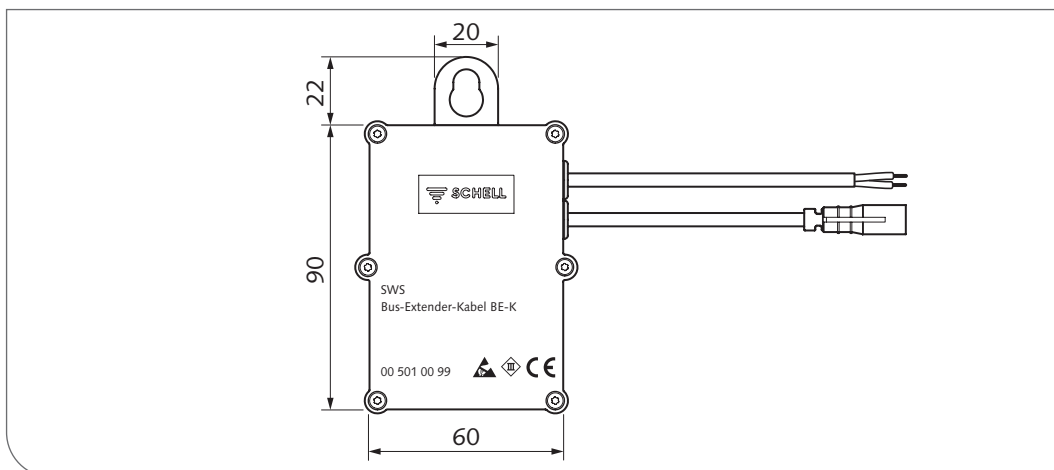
Extensor de bus SWS por cable BE-K. Dimensiones
